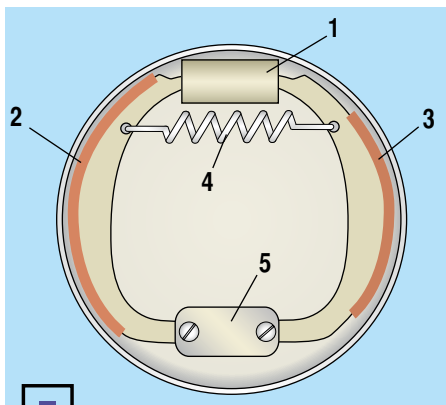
Механизм с шарнирным креплением колодок: 1 – колесный цилиндр; 2 – накладка передняя; 3 – накладка задняя (короче передней); 4 – стяжная пружина; 5 – узел шарнирного крепления колодок
